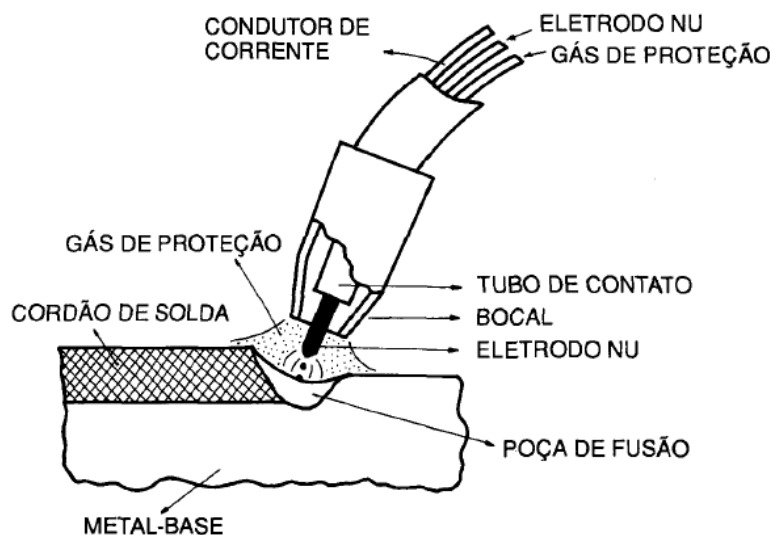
Esquemática da soldadura GMAW [10].
